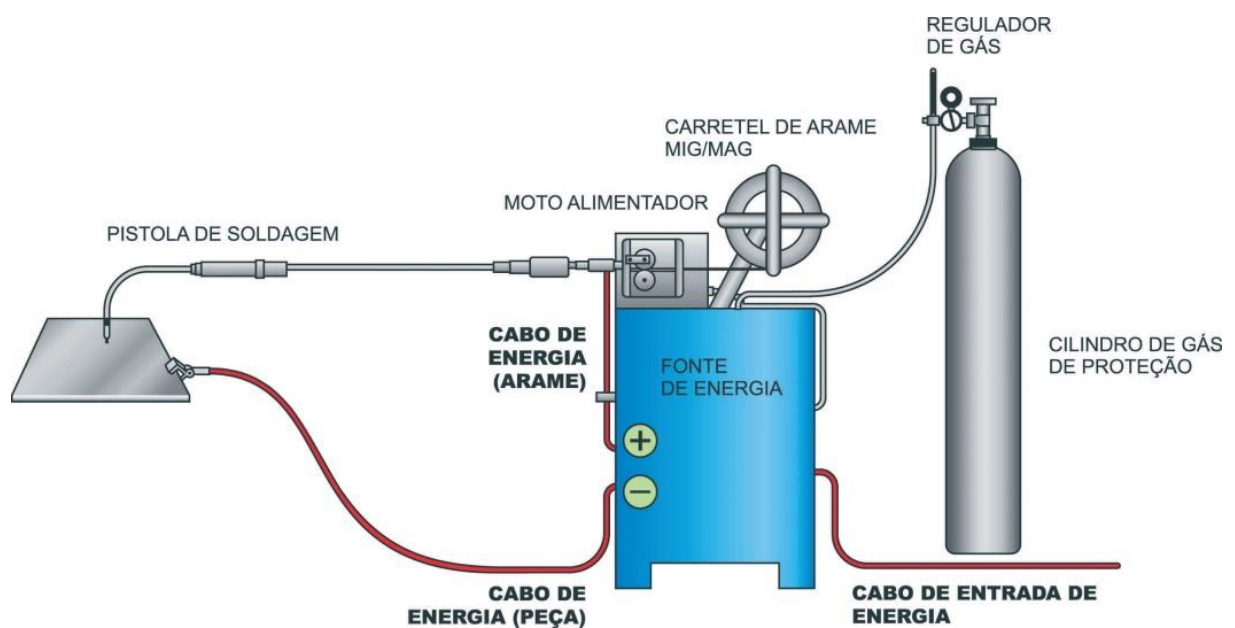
Esquema do posto de soldagem MIG/MAG.
